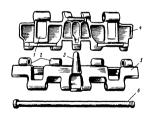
Элементы металлической многозвенной гусеницы с открытым металлическим шарниром: $1- \mbox{цевка}; \ 2- \mbox{ушки}; \ 3- \mbox{направляющий гребень}; \ 4, \ 5- \mbox{траки};$ $6- \mbox{соединительный палец}$
